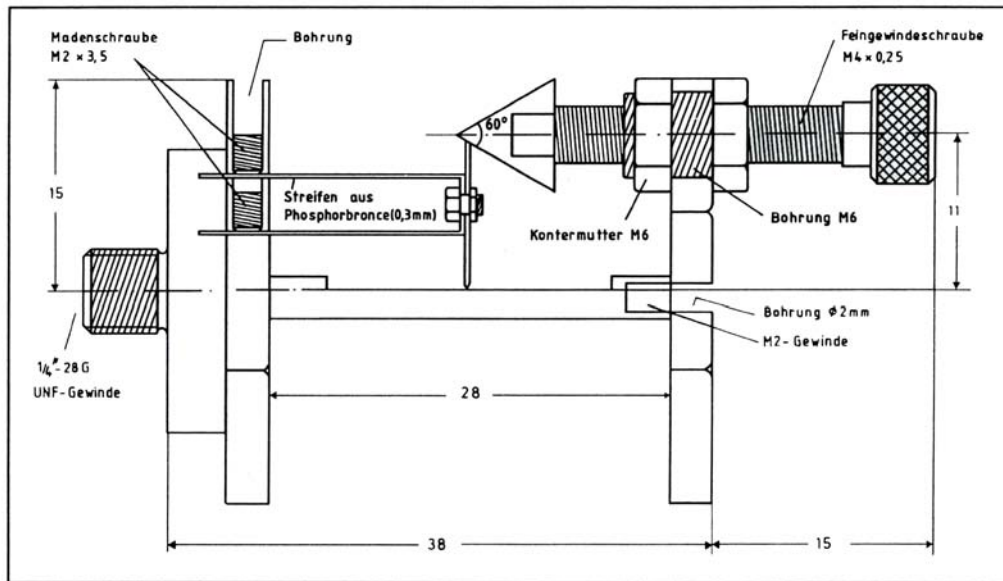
Skizze des Probenhalters für die Kompressorkühlmaschine
